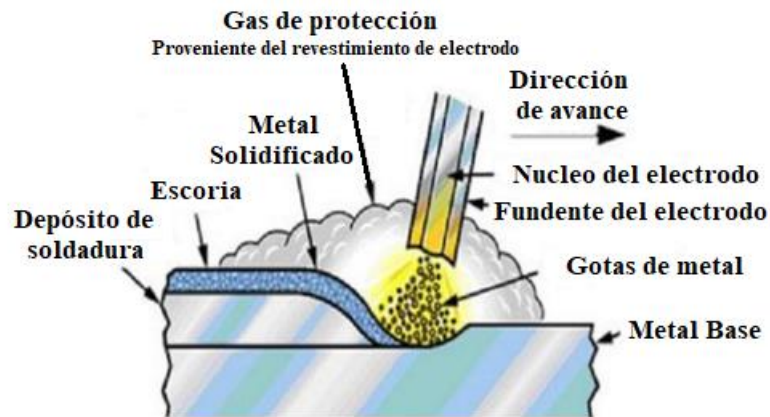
Elementos del proceso de soldadura SMAW [33].
